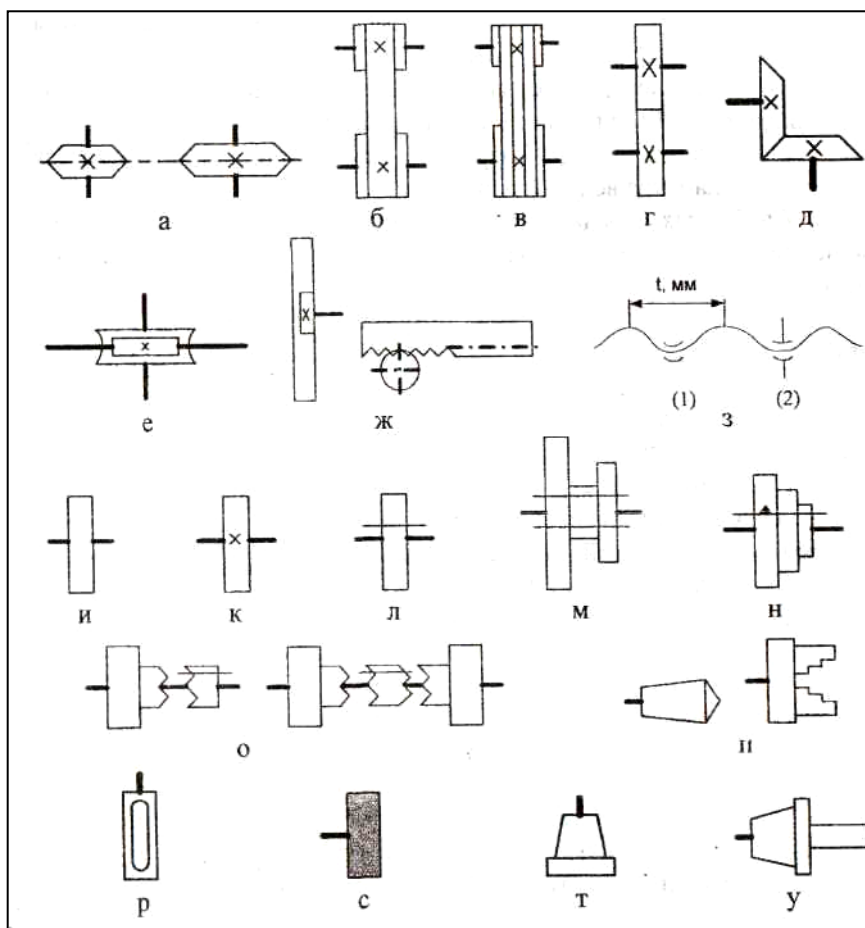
Условные обозначения элементов кинематических схем металлорежущих станков:
